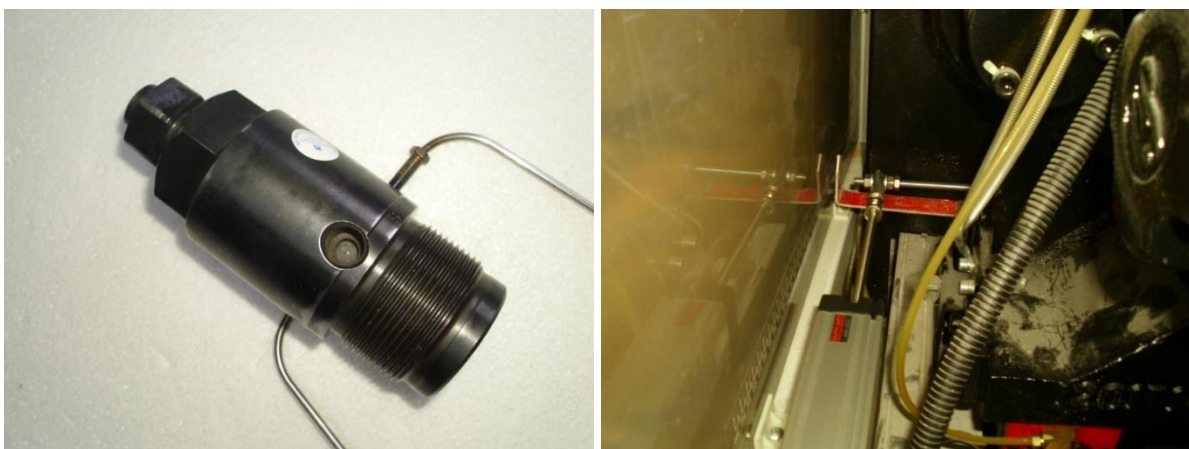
(links) FOS-Schmelzdrucksensor zur Messung des Einspritzdruckes in der Maschinendüse in Kombination mit einem FOS Schmelzethermometer und (rechts)
